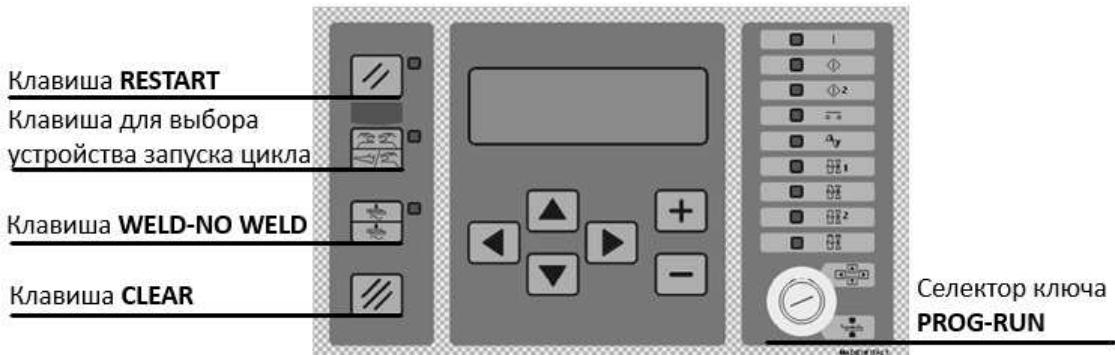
Панель блока управления сваркой TE526
